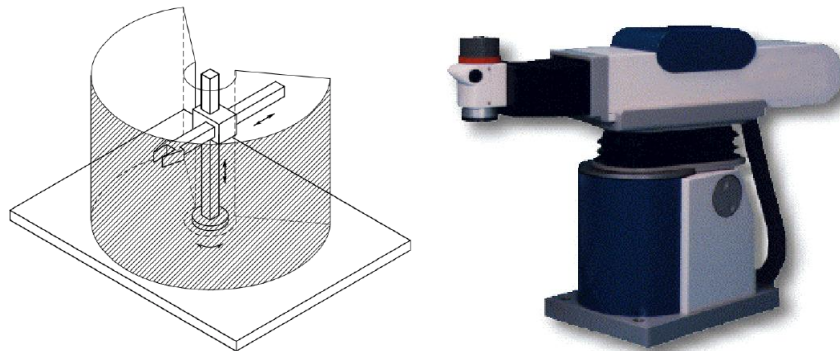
Manipulador Cilíndrico (RLL): (a) desenho esquemático; (b) Robô com configuração cilíndrica
